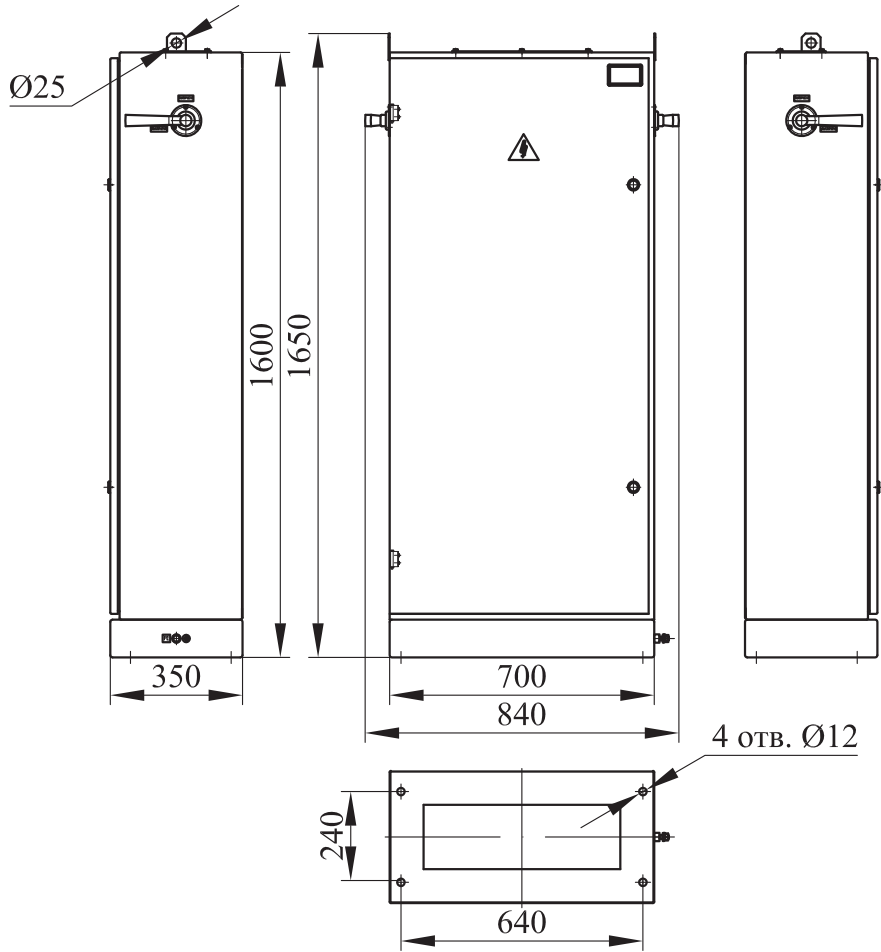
Габаритные и присоединительные размеры шкафов по схеме 19-23
